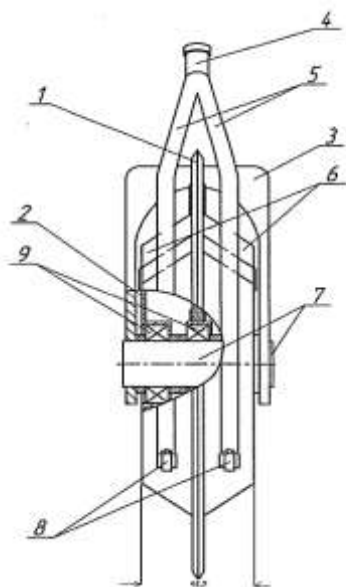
Однодисковый сошник с двухсторонними ребрами-бороздкообразователями для узкорядного посева:
